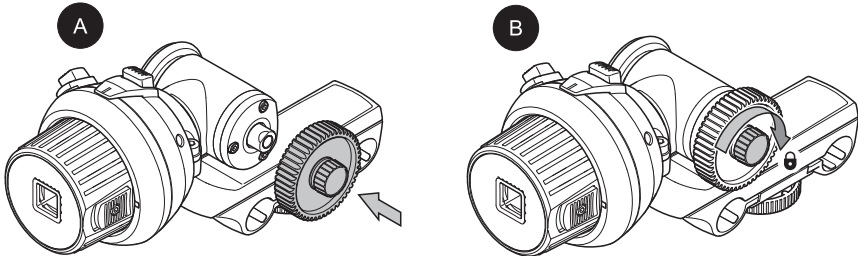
Montaje de la rueda de fricción y del engranaje impulsor
